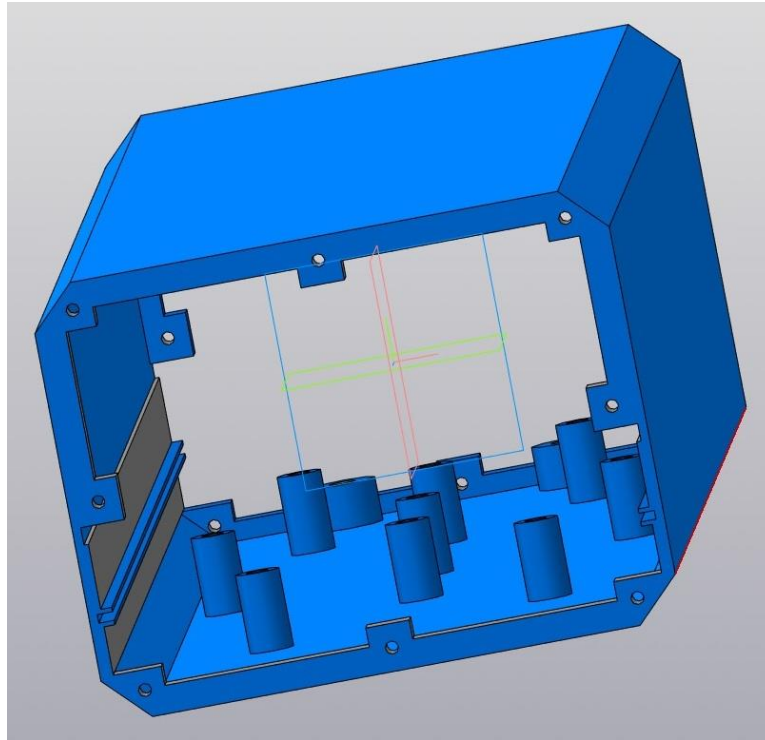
Додаткові потовщення на торцях головного корпусу для монтажу стінок
